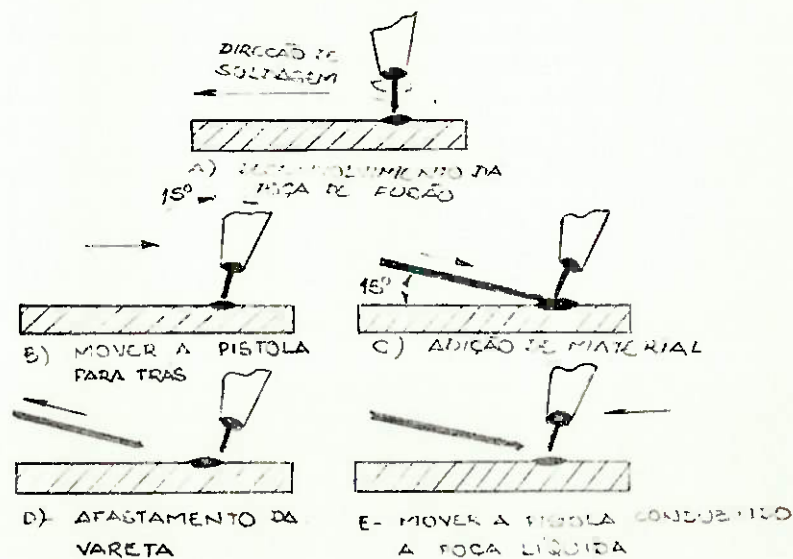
TÉCNICA PARA SOLDAGEM TIG MANUAL
